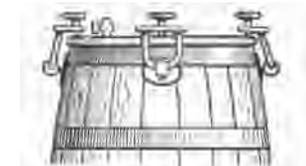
Fermeture ou couvercle d'une baratte rotative.
